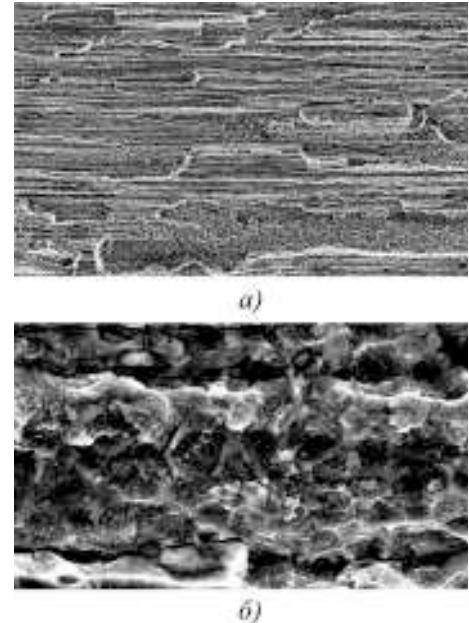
Строение излома сварного соединения прессованной полосы толщиной 40 мм, середина шва:
